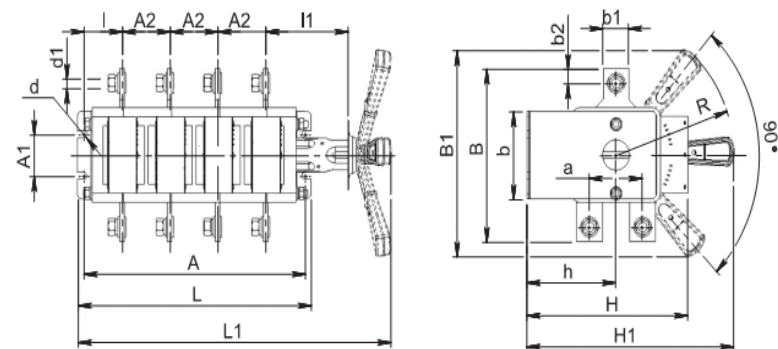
Б Выключатель-разъединитель на два направления 4-полюсный с боковой смещенной рукояткой
